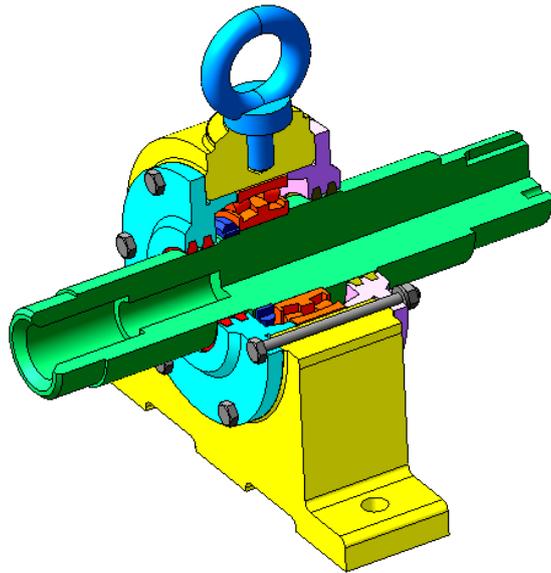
Трехмерная модель сборочного узла «Узел подшипниковый» в собранном виде
